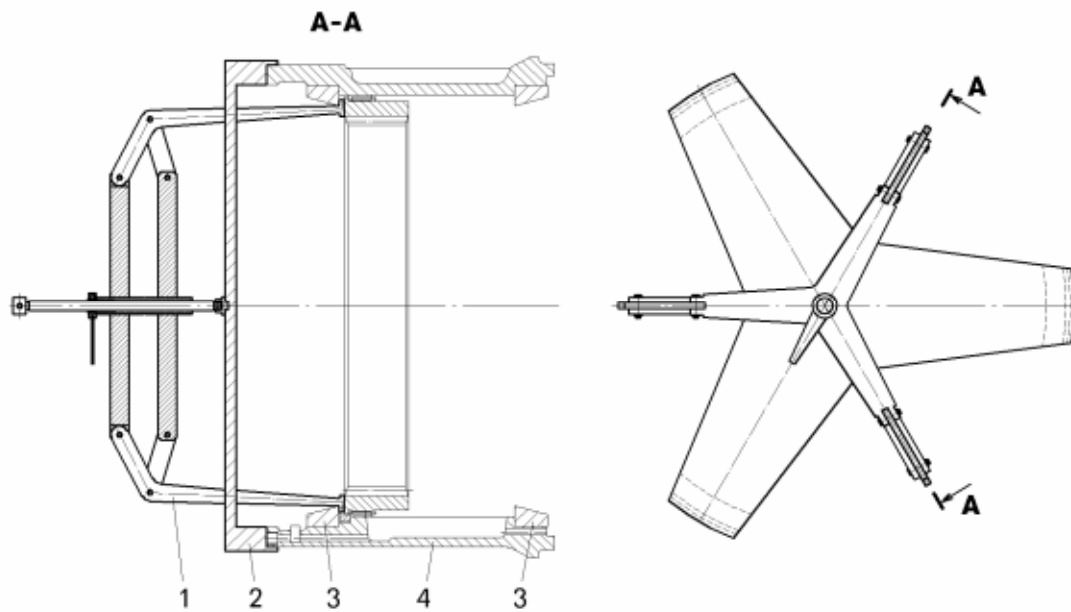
Приспособление для снятия наружных колец подшипников:
